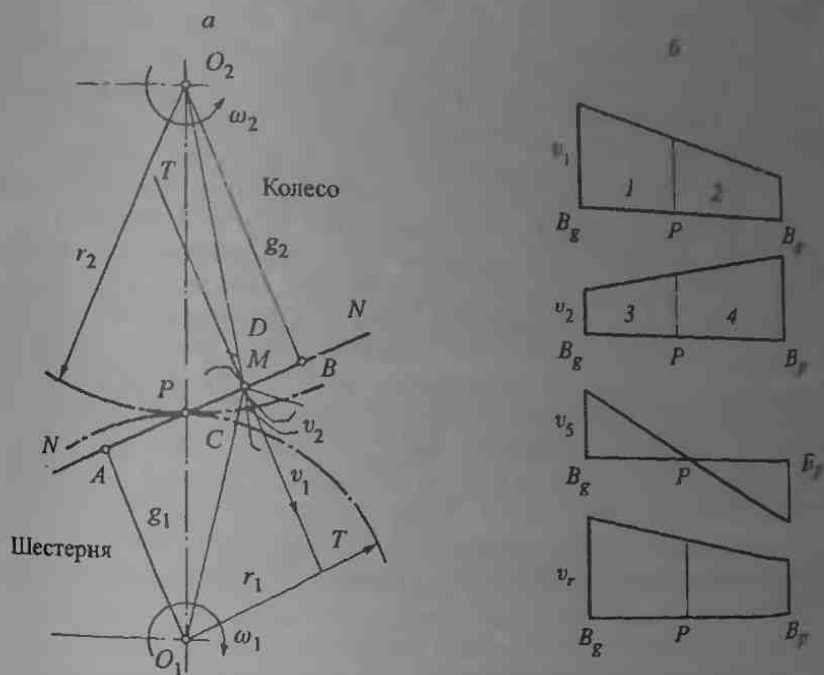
Схема зацепления зубьев эвольвентной передачи (а) и изменения скоростей скольжения и качения вдоль линии зацепления (б): 1, 2 — головка и ножка зуба шестерни; 3, 4 — ножка и головка зуба колеса
